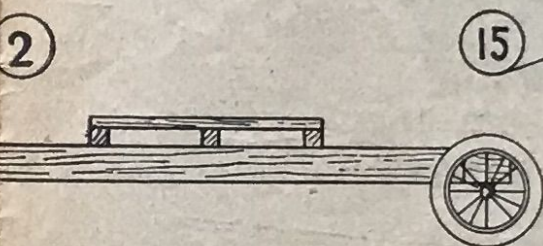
et 13. — Fixation du mât sur une planchette clouée sur le beaupré au point Y.
